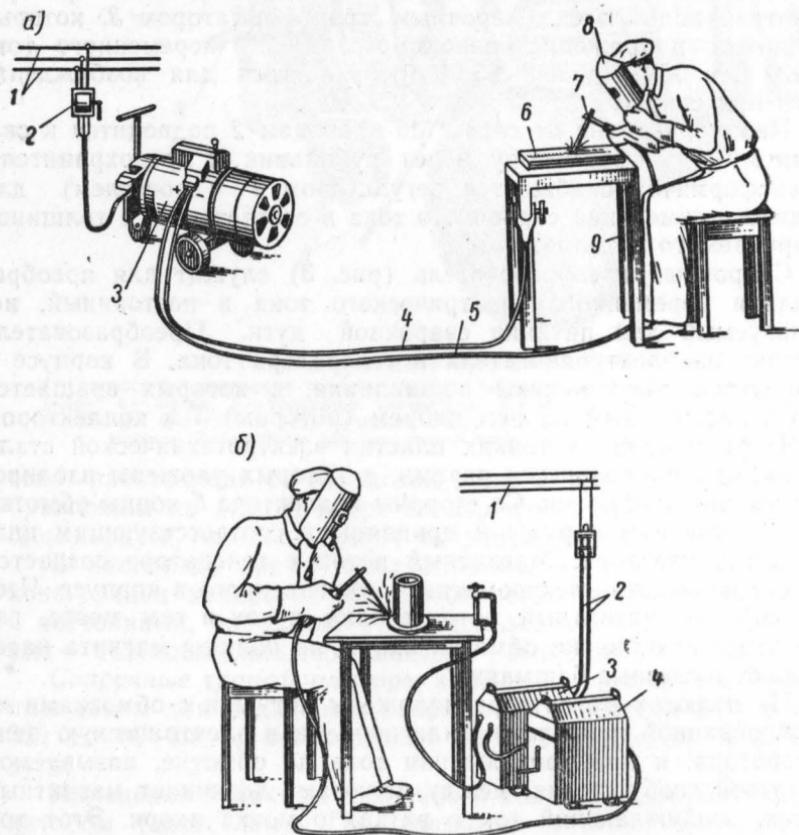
Сварочные посты для ручной электродуговой сварки
